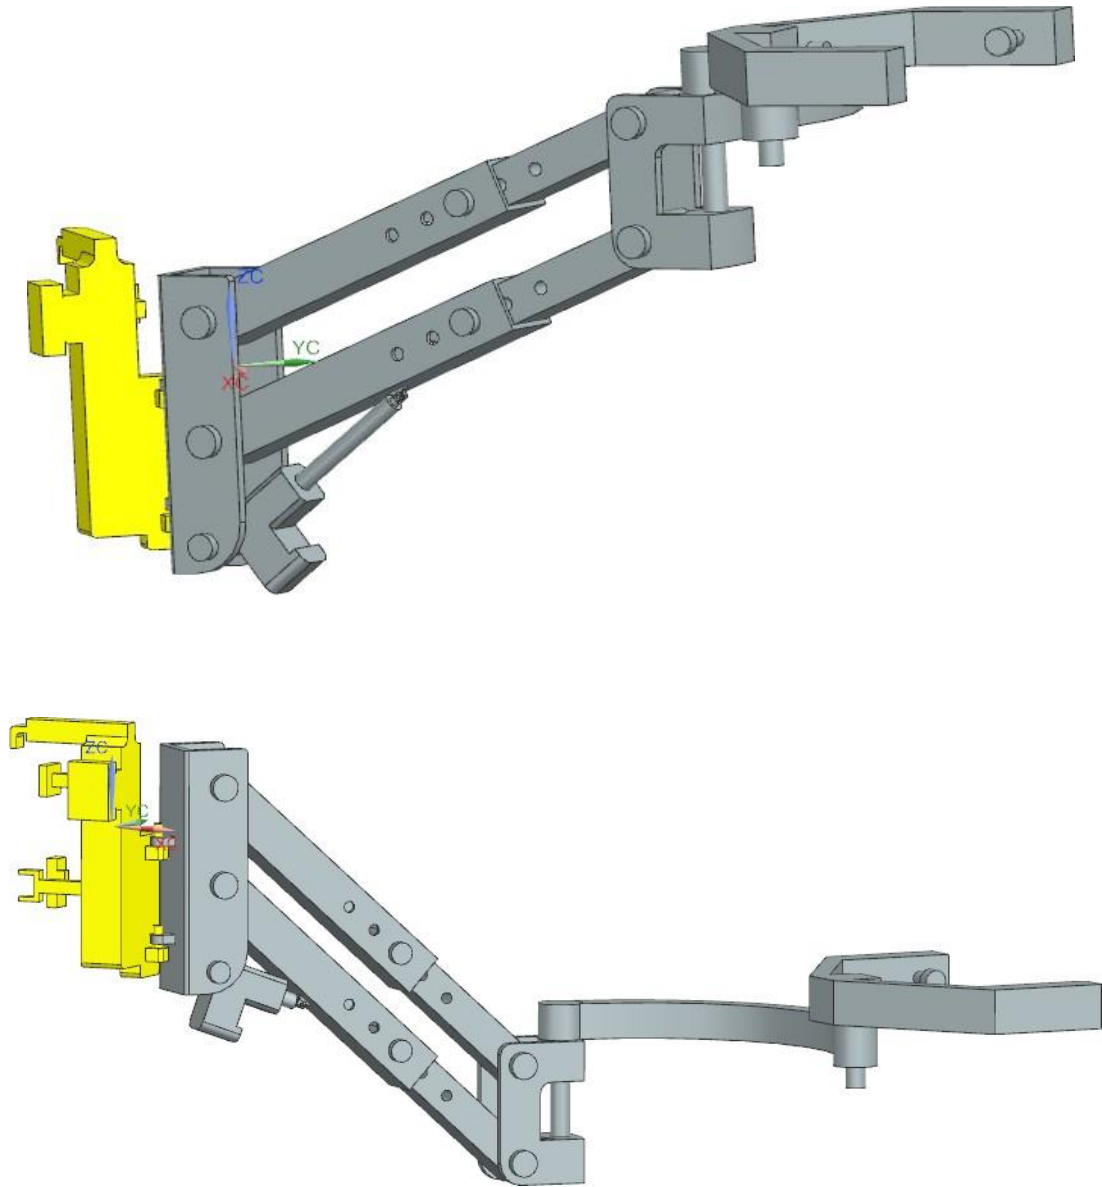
y 63. Dispositivo completo ensamblado en CAD.
